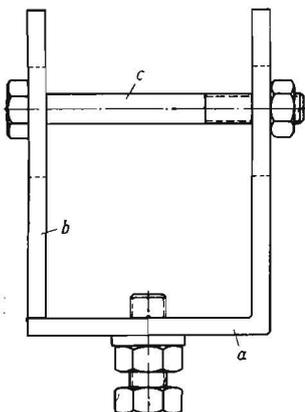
Verstärkung der Stelleinrichtung am Schneidwerk. a Winkel, b angeschweißte Platte, c Verbindungsschraube
